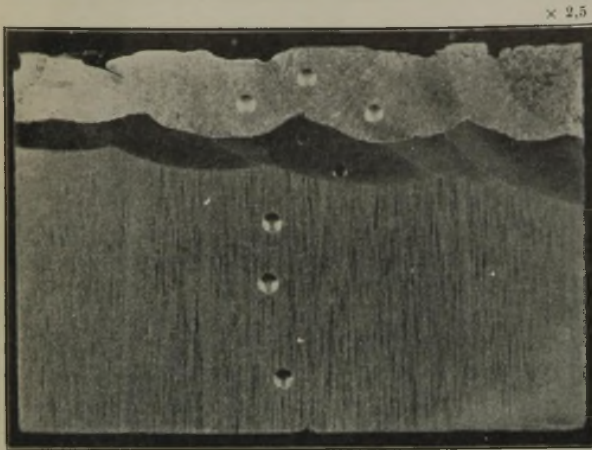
Brinellprüfung der Schweißstelle.
